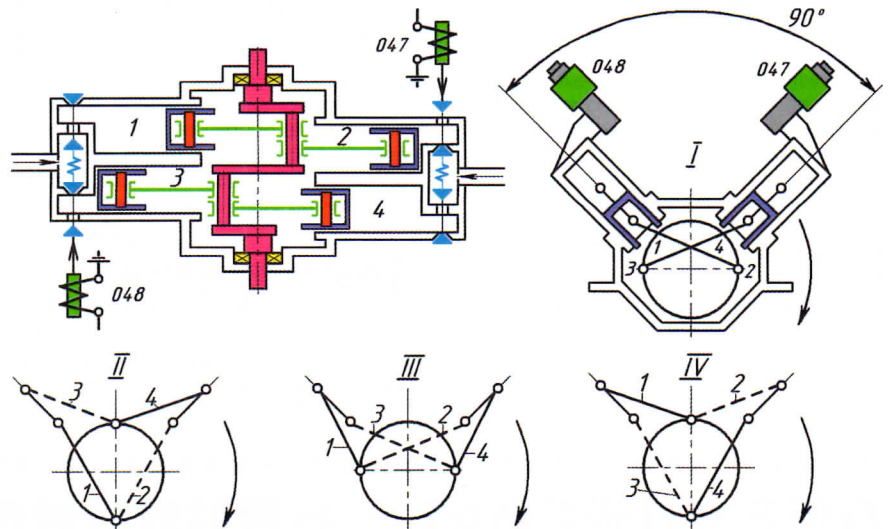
Схема работы привода: 1 — 4 — номера цилиндров; 047, 048 — вентили с воздухораспределителем 5VC; I — IV — фиксированные положения привода
